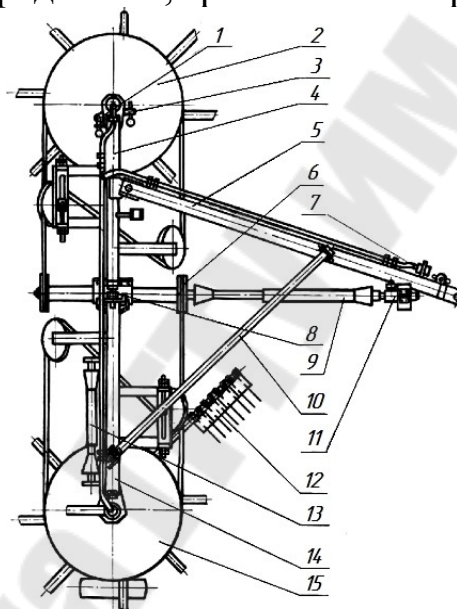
Грабли-ворошилки роторные ГВР-630: 1, 3 – фиксаторы; 2 – ротор левый; 4 – рама левая; 5 – сннца; 6 – передача клиноременная; 7 – гидросистема; 8 – болт регулировочный; 9 – передача карданная; 10 – штанга; 11 – передача цепная; 12 – граблина; 13 – вал карданный; 14 – рама правая; 15 – ротор правый
